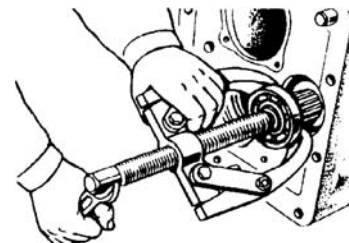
Спресовка подшипника № 50308, снятие вала I передачи и заднего хода, замена ведомой шестерни включения ходоуменьшителя, скользящей и ведомой шестерни I передачи и заднего хода.
